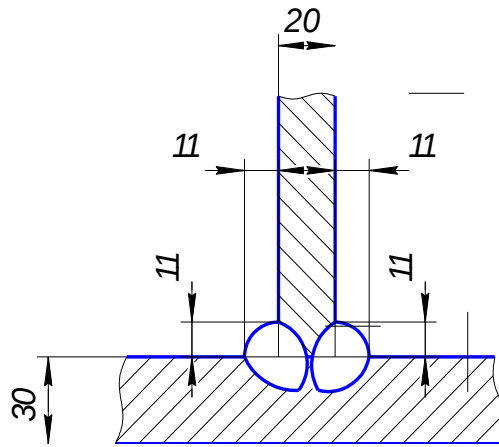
Конструктивні елементи з'єднання ТЗ
